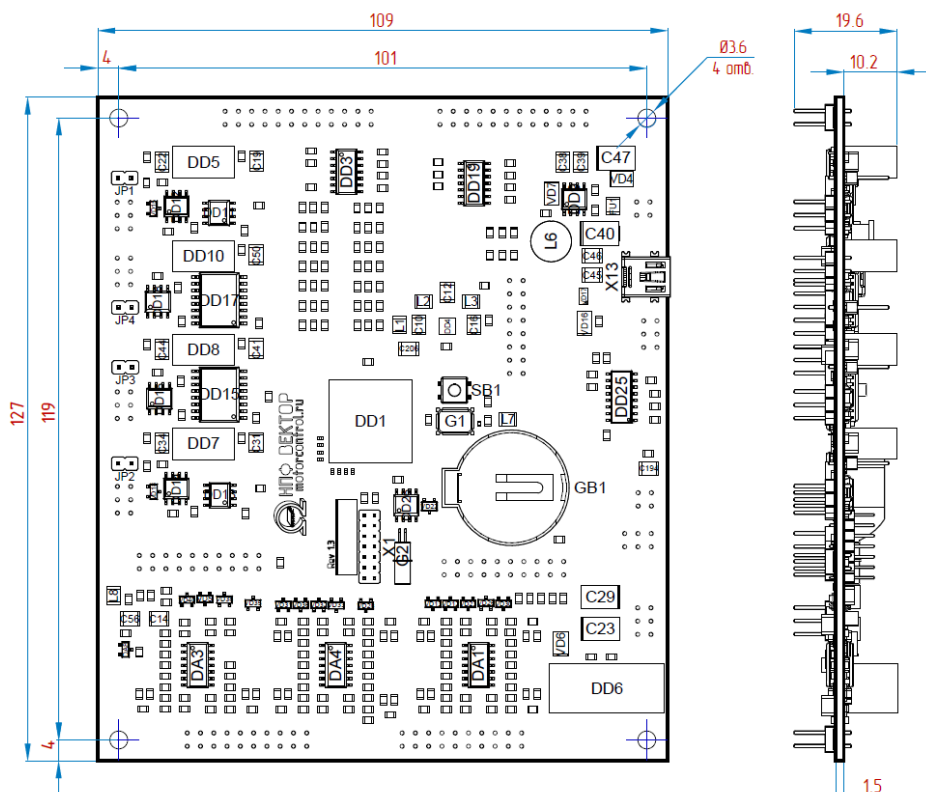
Габаритные и присоединительные размеры платы контроллера МК50.1
